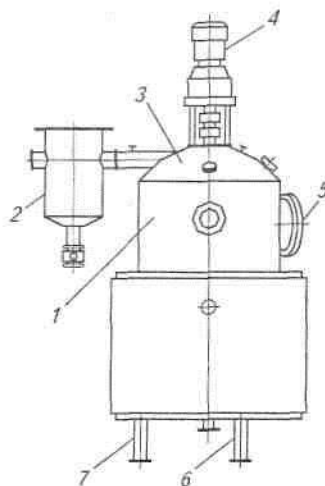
Схема вакуум-кристаллизатора: 1 - вертикальный цилиндр; 2 - ловушка; 3 - крышка; 4 - привод; 5 - технологический штуцер; 6 - сливной штуцер; 7 - опоры.
